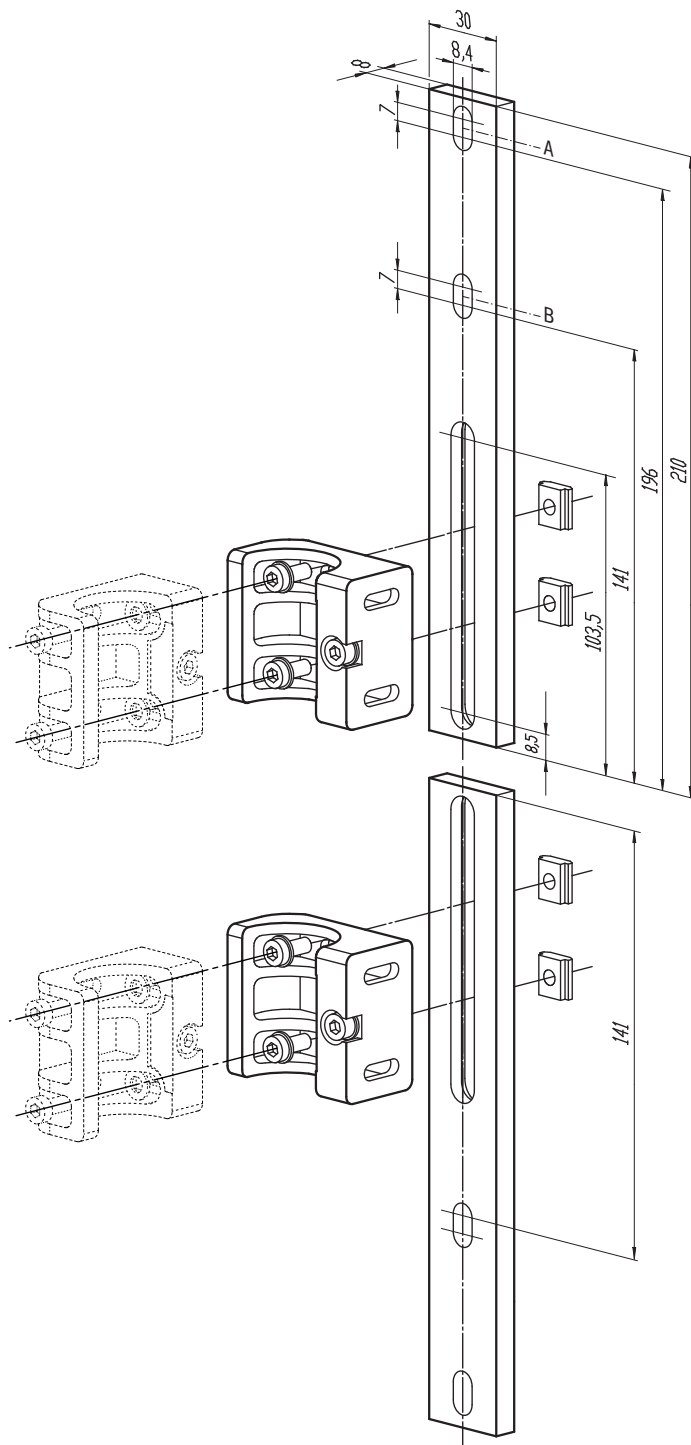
Габаритный чертёж сменного держателя (2071021)
